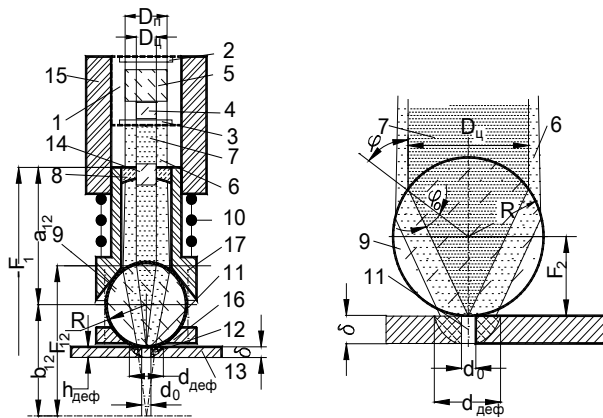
Схема ЛТУ для якісної обробки отворів в металевих заготовках малої товщини:
